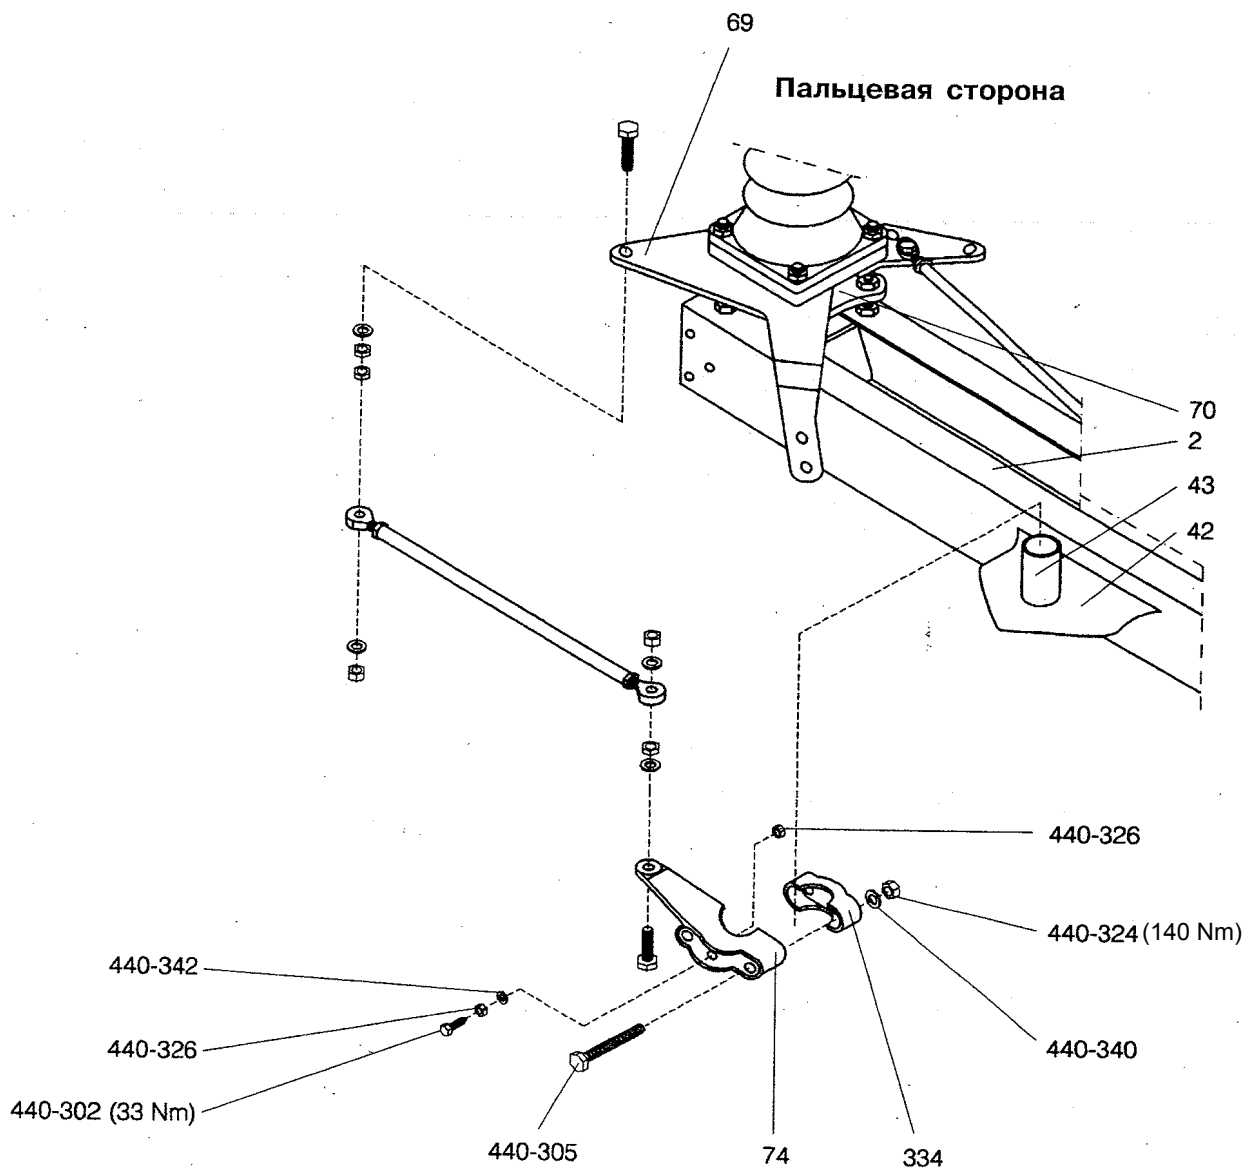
Установка приводного механизма разъединителя; раздельная установка. Установка приводного рычага (74) при расположении приводного механизма на стороне противоположной открыванию
